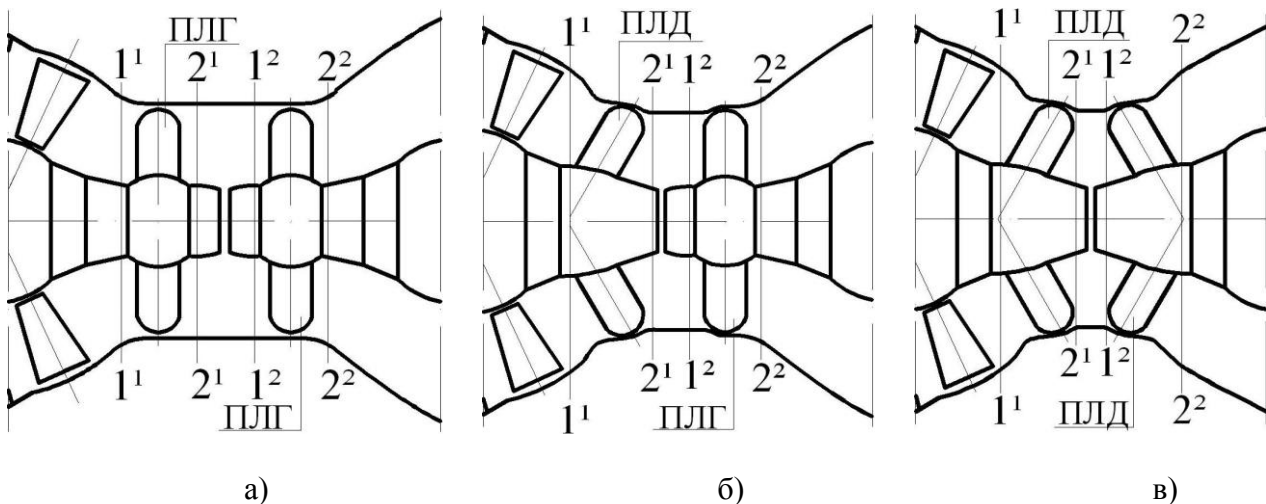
Схема компоновки робочих коліс і розрахункові перетини зведеного прямооточного гідроагрегату.
